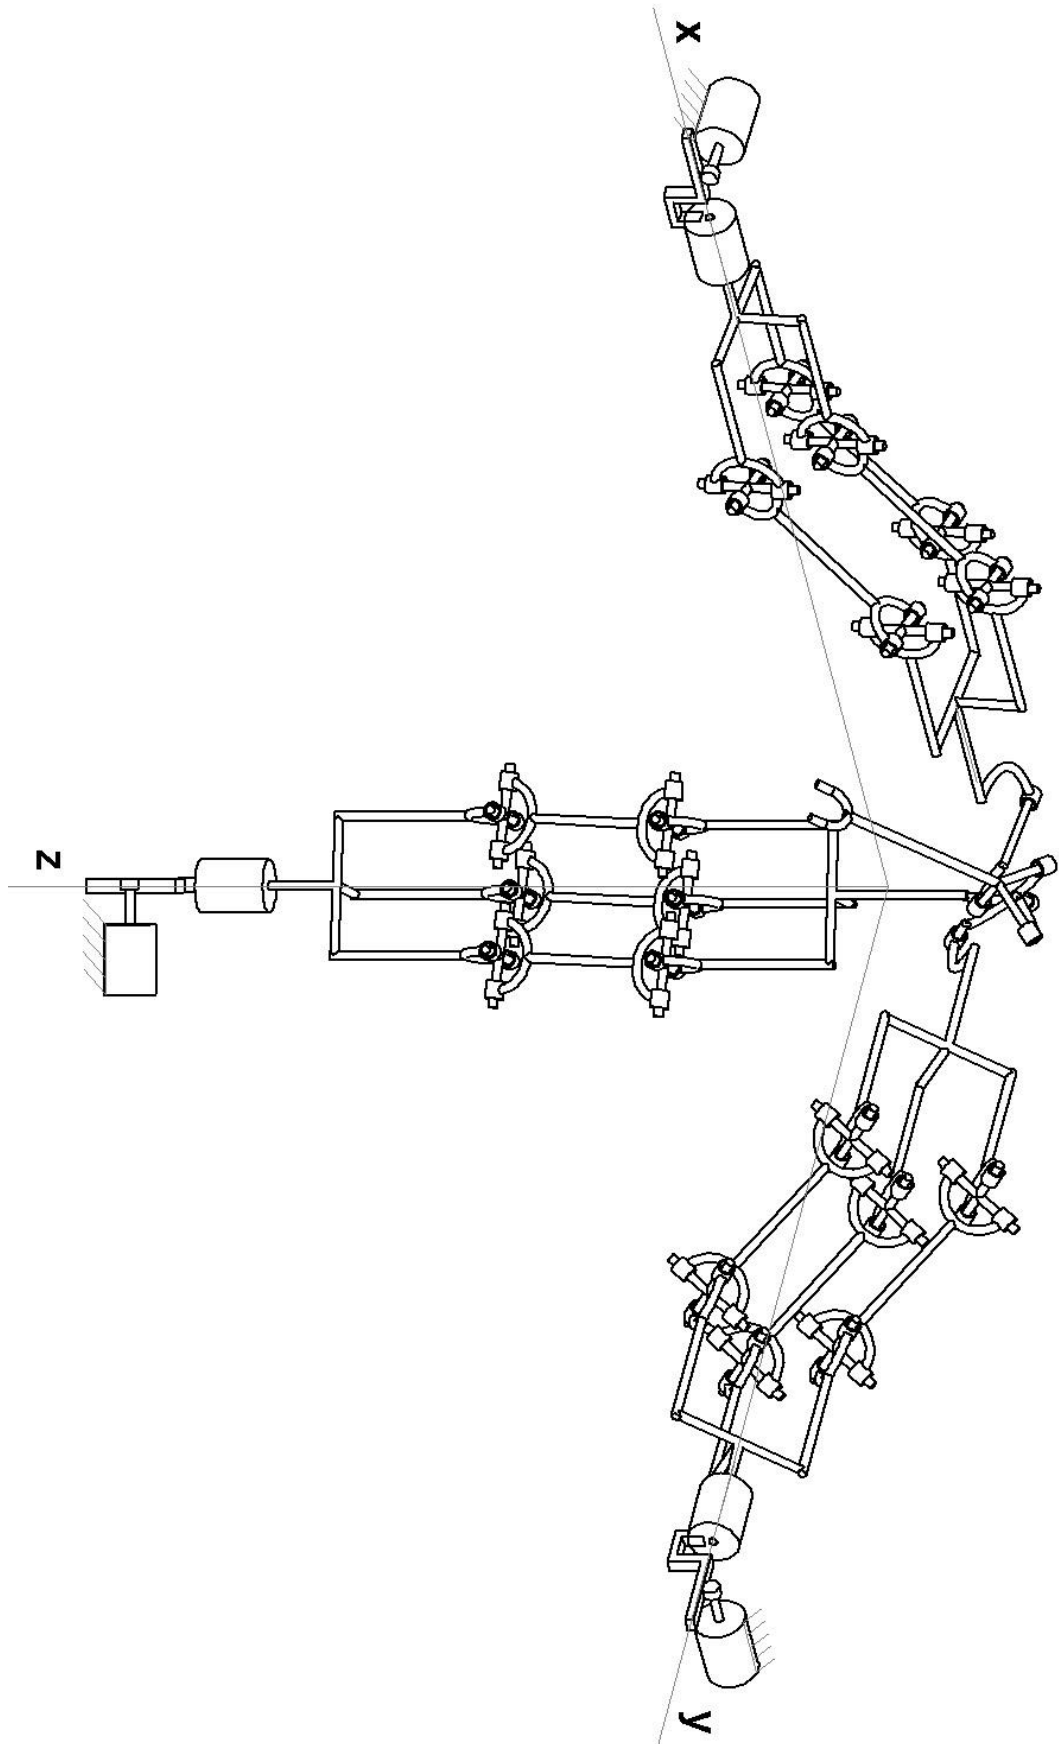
б. Механизм с кинематической развязкой между поступательными и вращательными движениями выходного звена с тремя карданными валами в каждой кинематической цепи.
